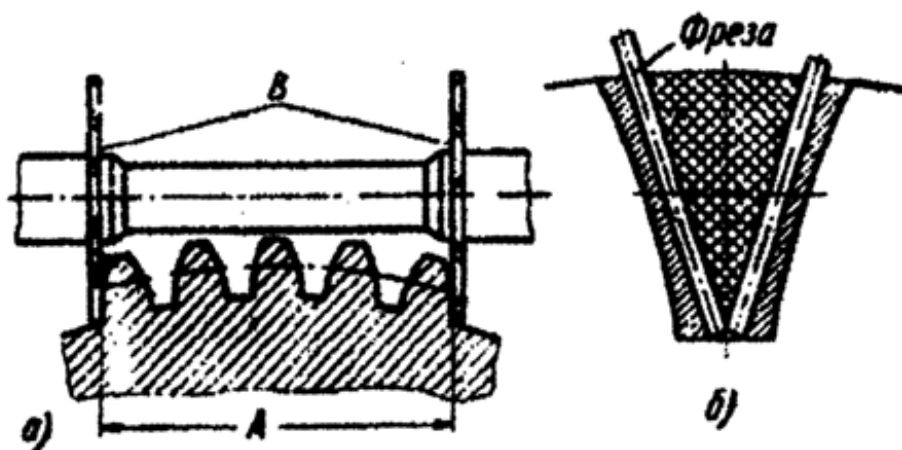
Прорезка впадин крупномодульных зубчатых колес двумя трехсторонними дисковыми фрезами:
